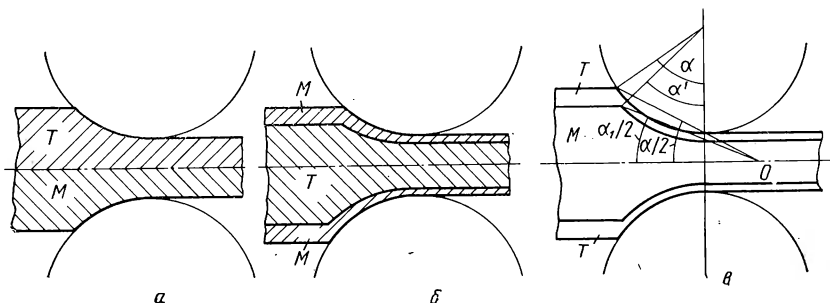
Способы прокатки двухслойных и трехслойных металлов
